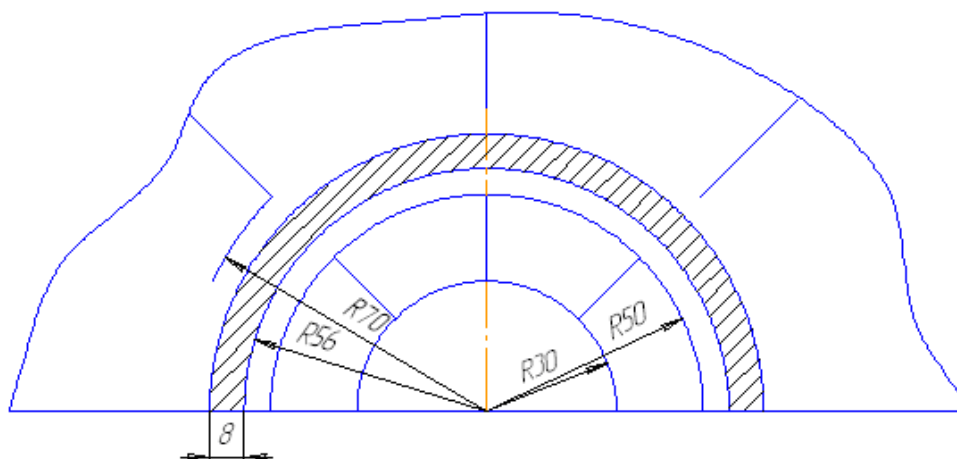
Размеры импеллера типового дробеметного колеса
